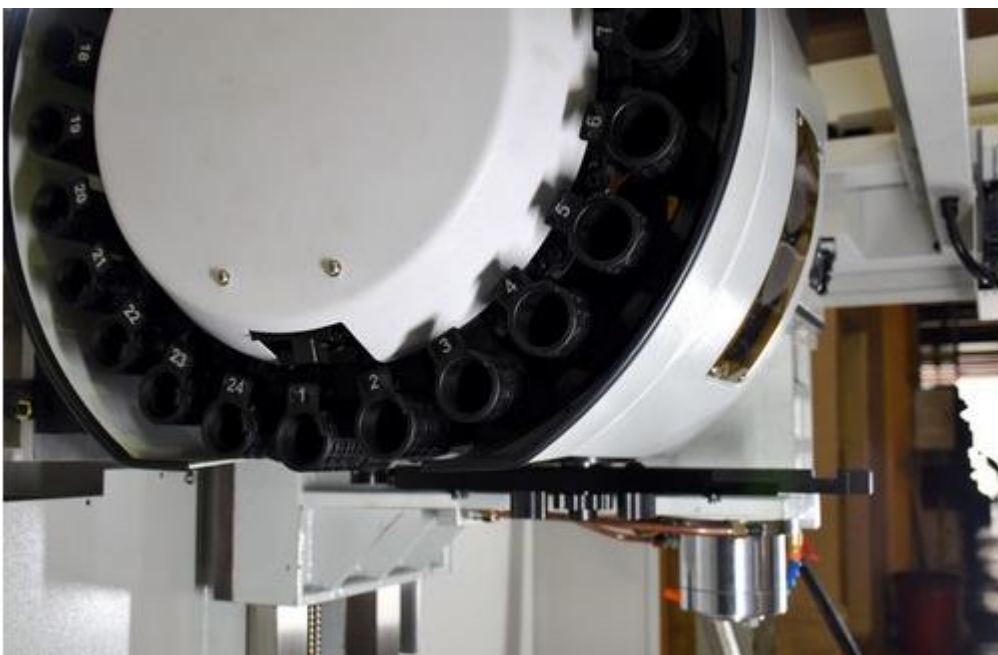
Механизмы смены инструментов вертикальных станков типа «РУКА» с инструментальным магазином барабанного типа
